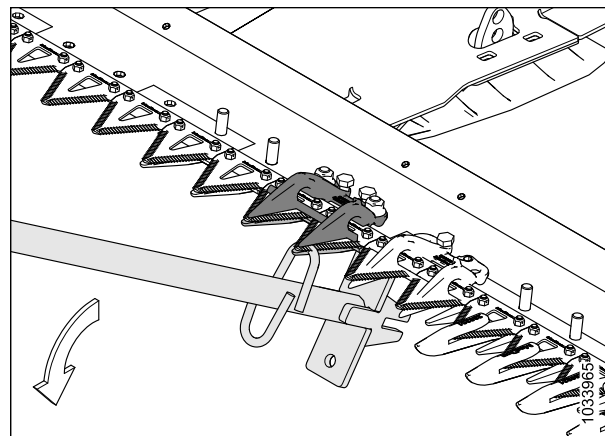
Регулировка смещением вниз — укороченный противорежущий палец
